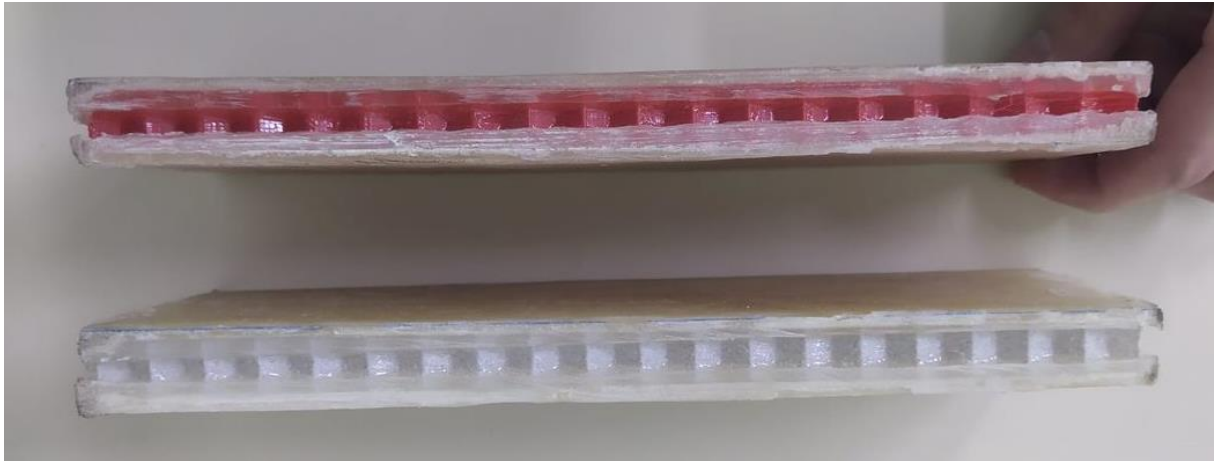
Painéis sanduíche vista lateral - Fonte: (Autor)
